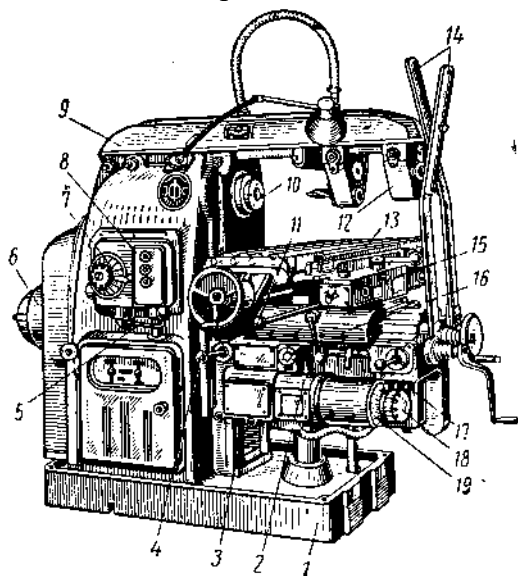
Универсально-фрезерный станок мод. 6Н82
